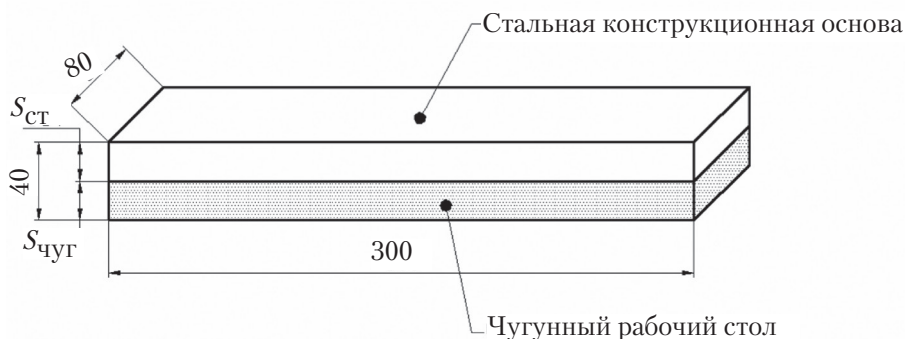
Эскиз опытной биметаллической отливки для исследования напряжённого состояния и процесса разрушения
